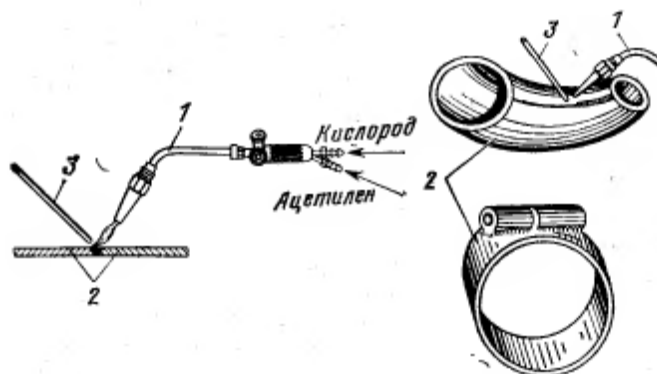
Схема кислородно-ацетиленовой сварки:
